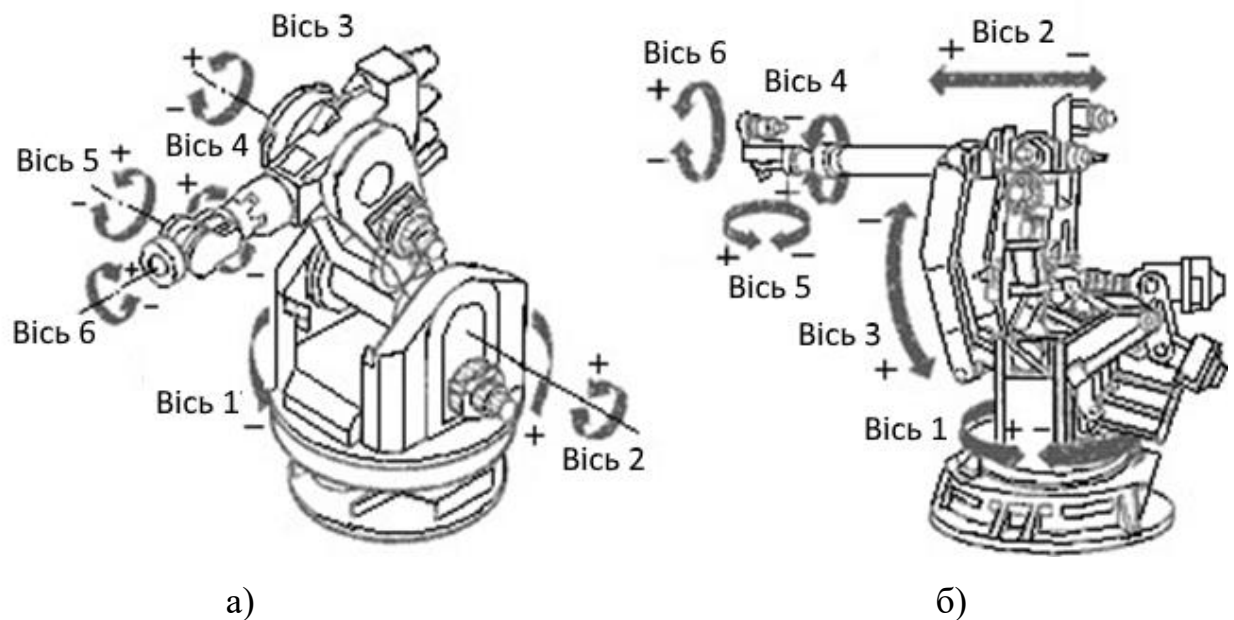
Ступінь рухомості зварювального робота типу IR-160/60 (а) та IR-601/60 (б) німецької фірми "Кука"
